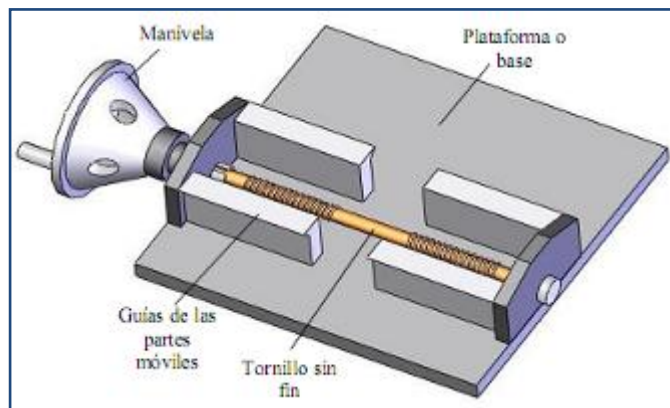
Despiece de máquina soldadora de termoplásticos.
